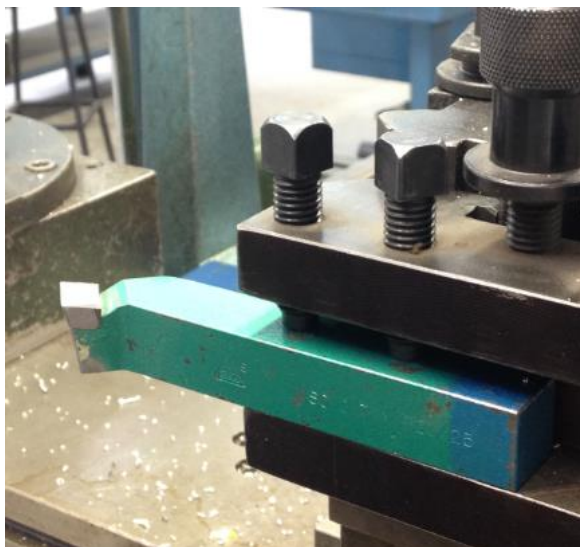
plaquita soldada ISO 2 TTM P20/25
